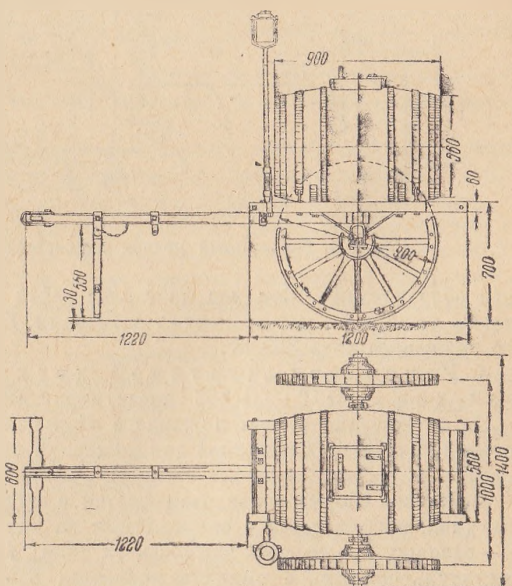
Бочечный ручной двухколесный нерессорный ход.
